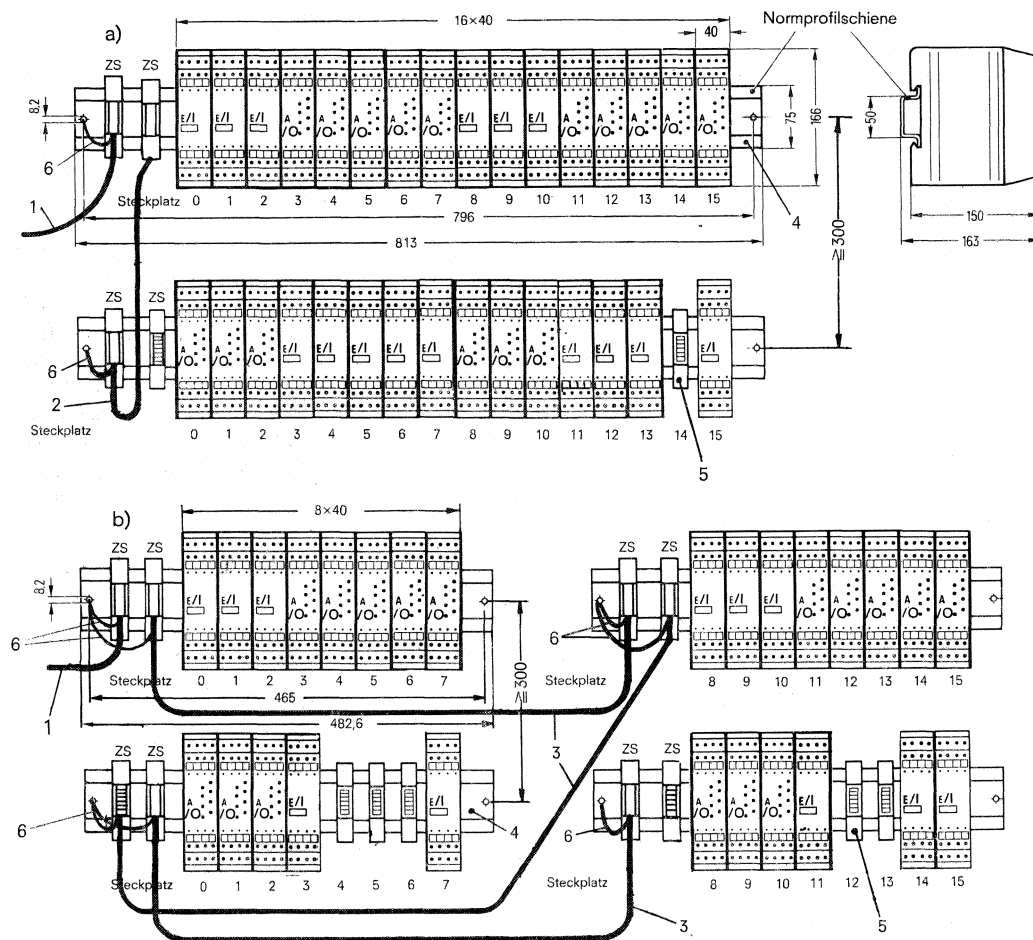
Ausbau der Peripheriebaugruppen für einen Stecker der Zentralbaugruppe a) mit langen Baugruppenträgern b) mit kurzen Baugruppenträgern
